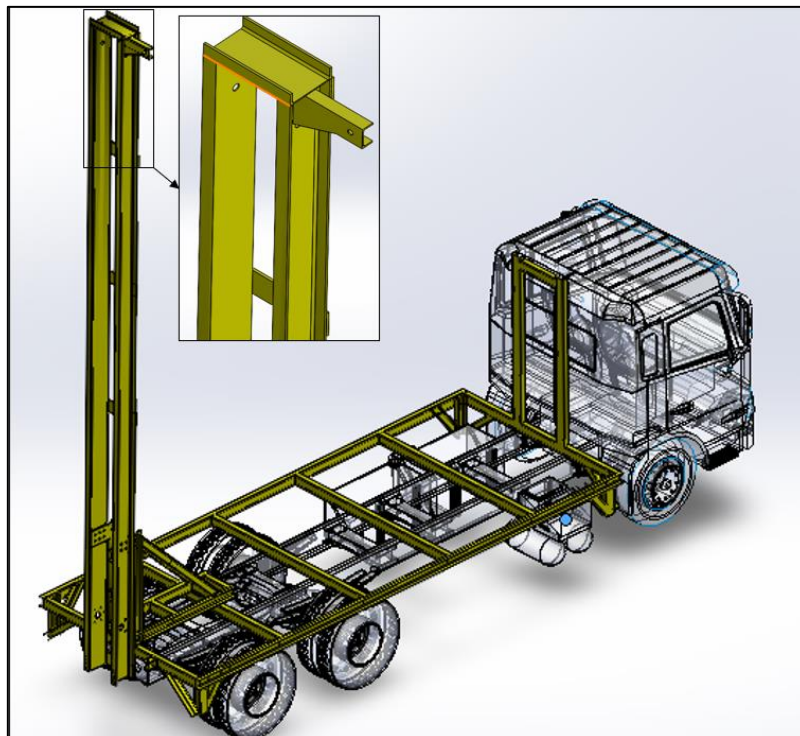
estrutura metálica da máquina (torre e plataforma)
